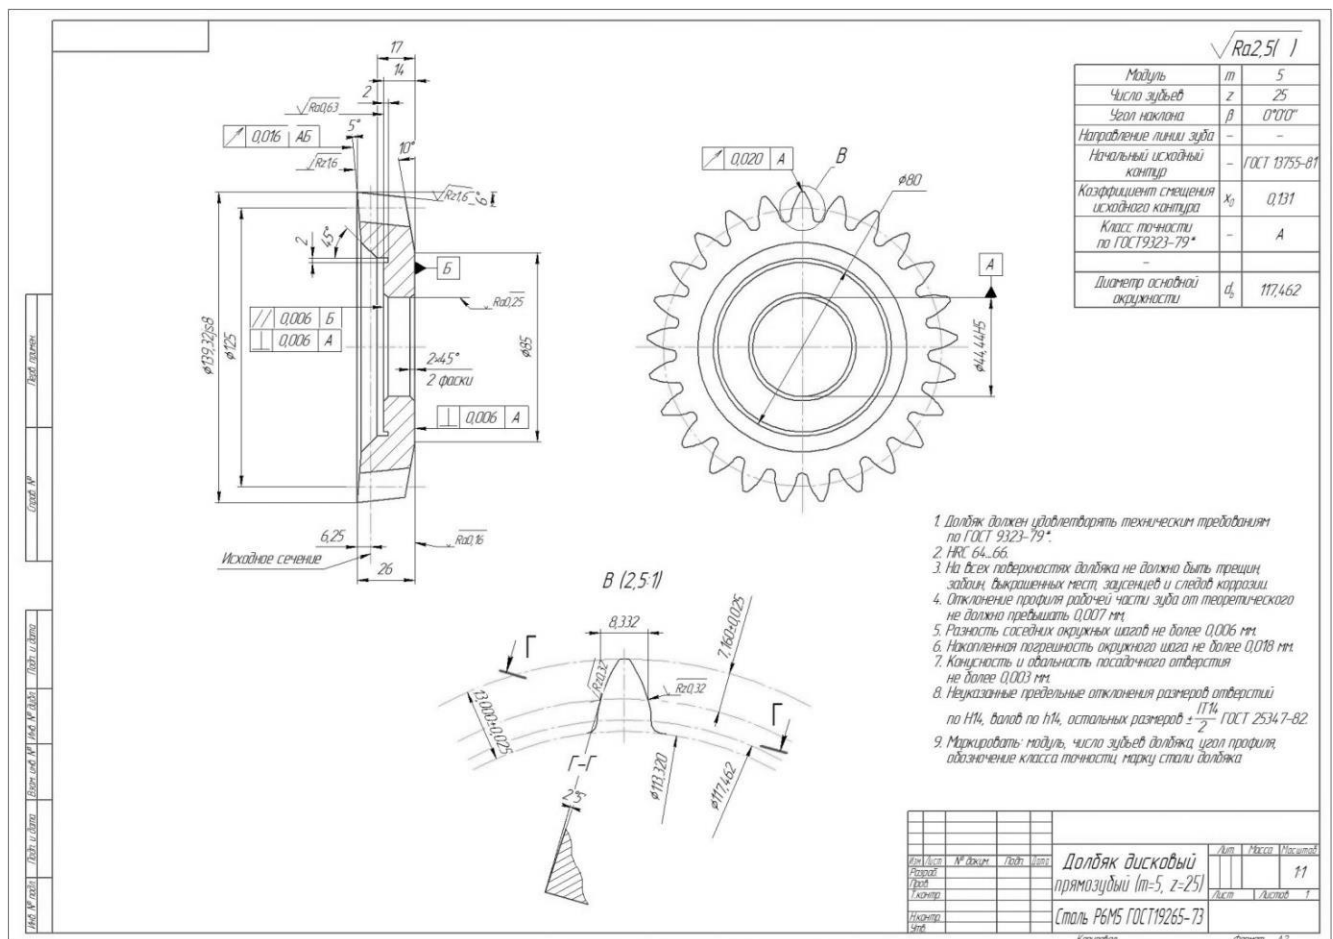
Чертеж конструкции сборного долбяка
